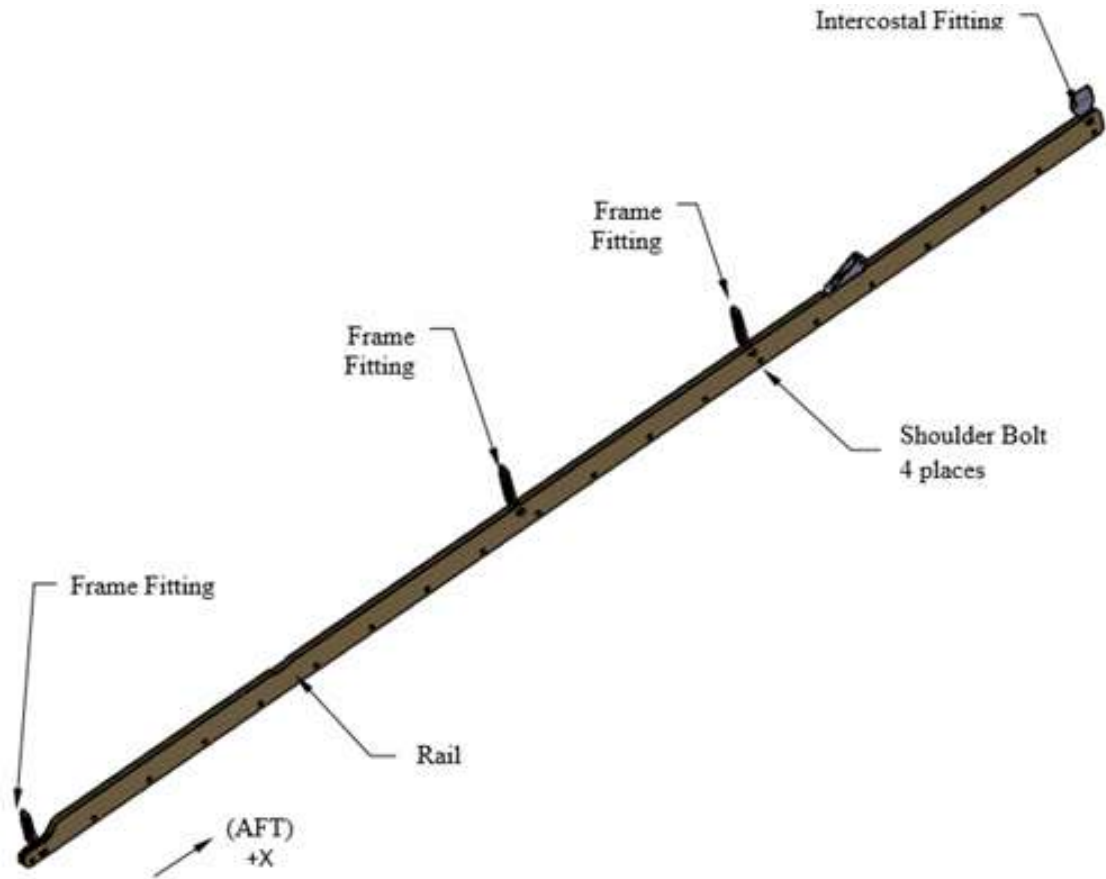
Розташування з'єднання рейки з Frame-Fitting
